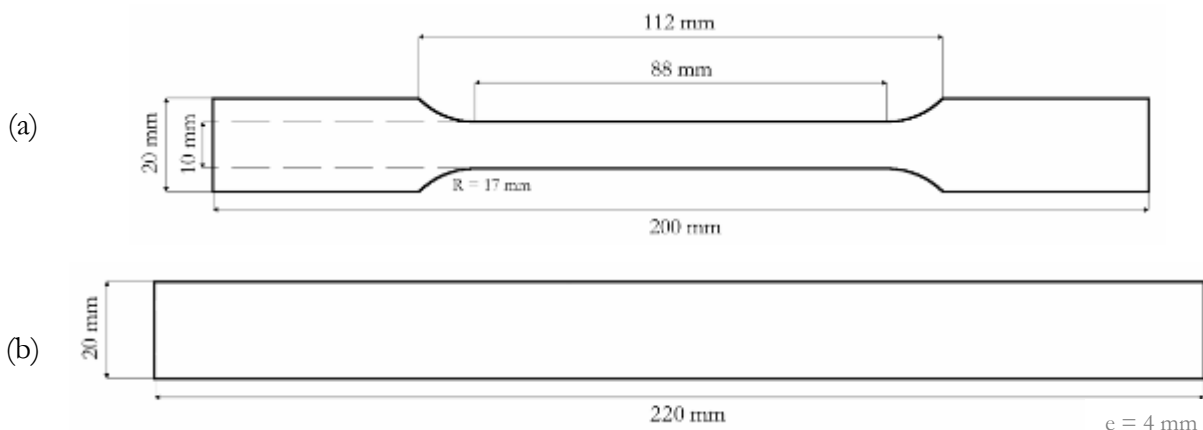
10. Dimensions des éprouvettes de type haltère (a) ou rectangulaire (b)
